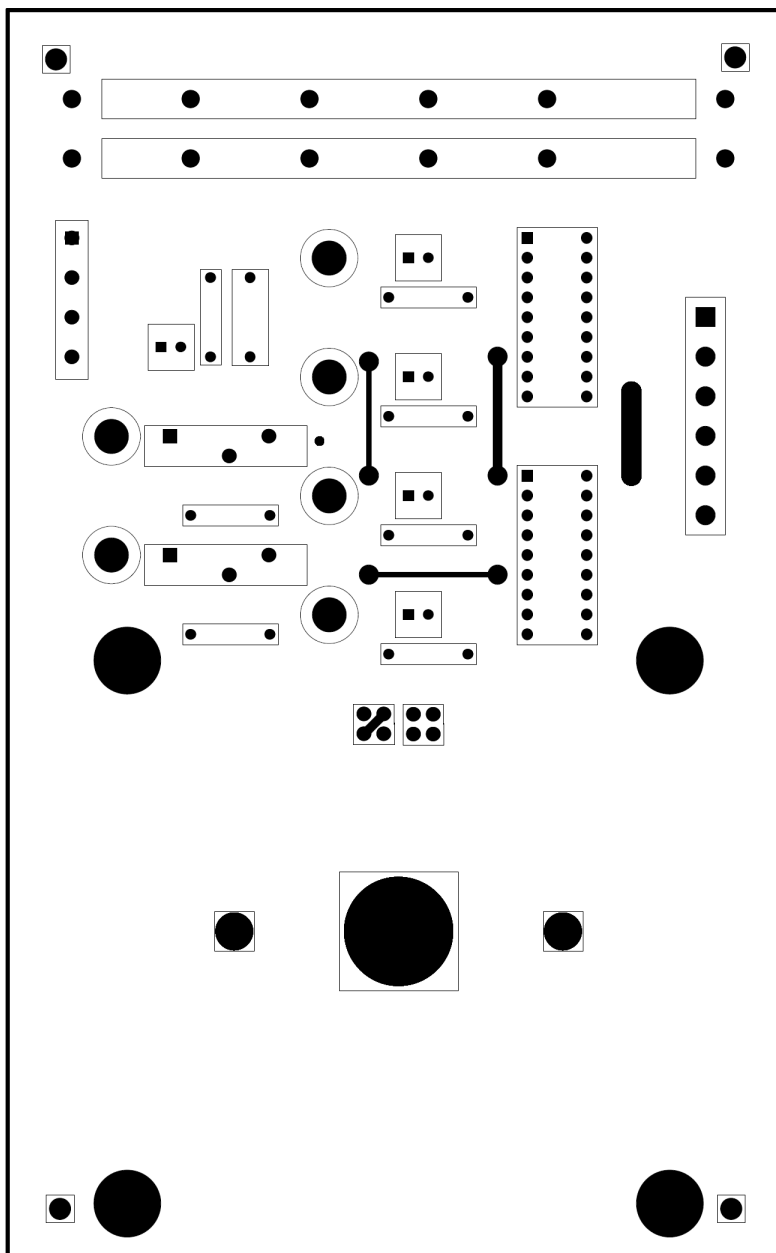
Capa superior (TOP) de la PCB de la interfície per al motor unipolar
